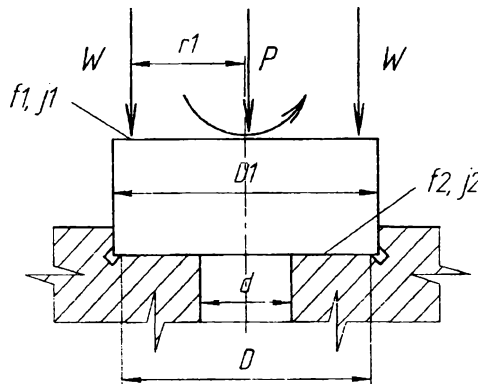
Схема сил, действующих на заготовку при ее установке по наружной поверхности
